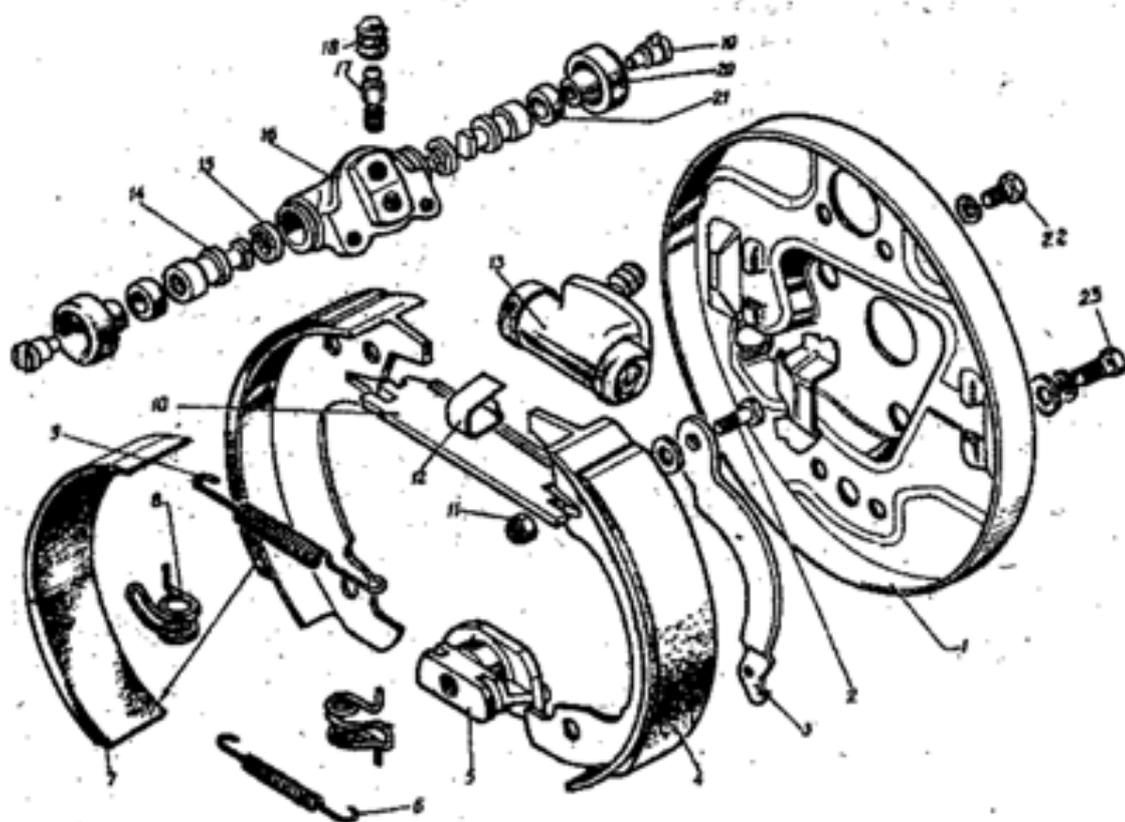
Детали заднего левого тормоза: 1 - шит тормоза; 2 - болт крепления рычага разжимного; 3 - рычаг; 4 - колодка тормоза; 5 - опора колодок; 6 - пружина нижняя; 7 - накладка фрикционная; 8 - пружина прижимная колодок; 9 - пружина верхняя; 10 - планка распорная; 11 - гайка; 12 - пластина демпферная; 13 - цилиндр в сборе; 14 - поршень; 15 - кольцо упорное; 16 - цилиндр; 17 - клапан выпуска воздуха; 18 - колпачок защитный; 19 - стержень; 20 - колпак; 21 - манжета; 22 - болт крепления цилиндра; 23 - болт крепления опоры колодок.
